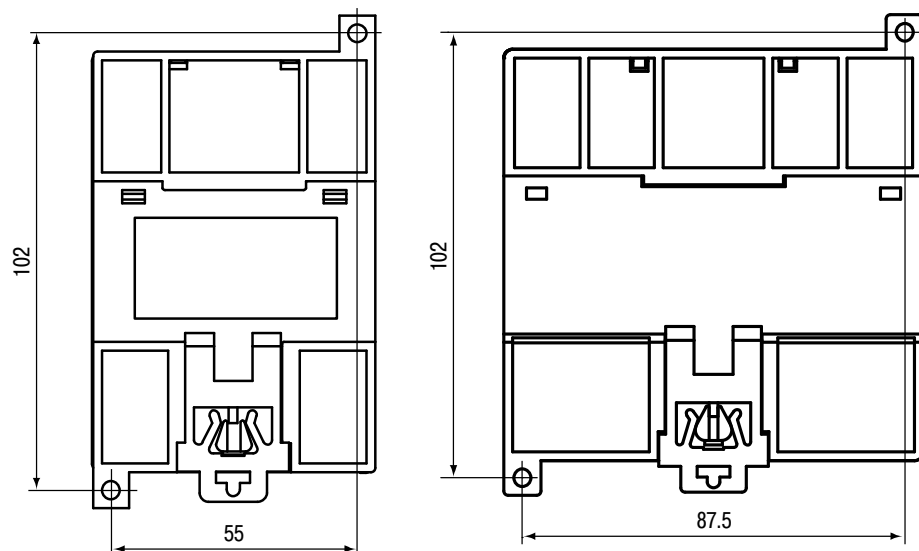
Montagemaße PR110-24.8D.4R (links) und PR110-24.12D.8R (rechts)
